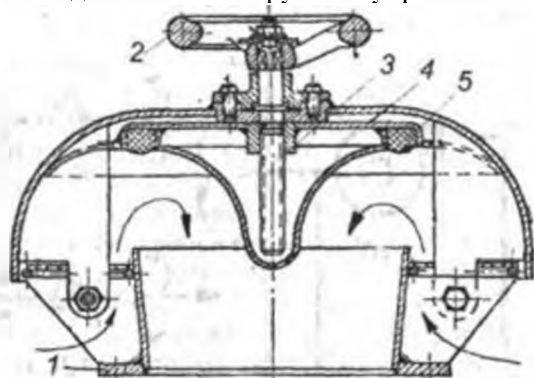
Схема грибовидной головки с ручным управлением: 1 - приёмный воздуховод; 2 - маховик ручного привода; 3 - шток; 4 - тарелка; 5 - прокладка.
